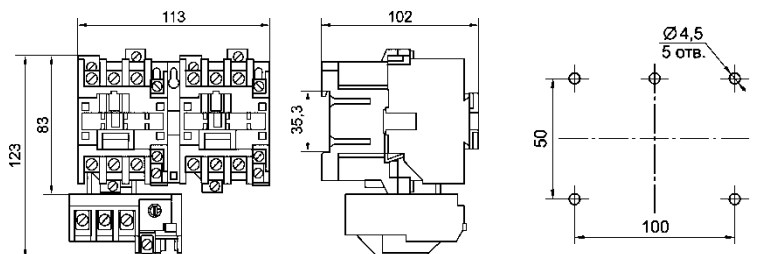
Пускатель реверсивный ПМ12-025 25А. Степень защиты - IP00; IP20.
